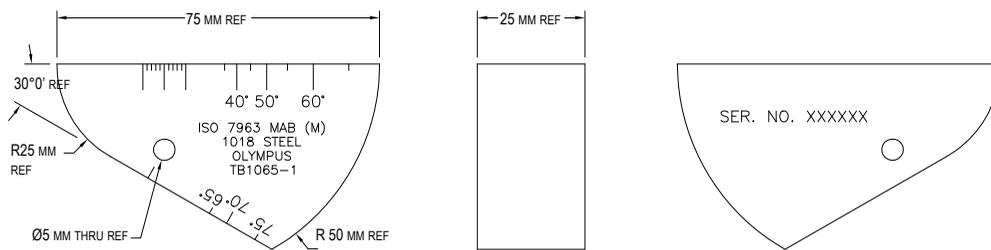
Калибровочный образец ISO 7963 MAB (Арт.: ТВ1065-1)
